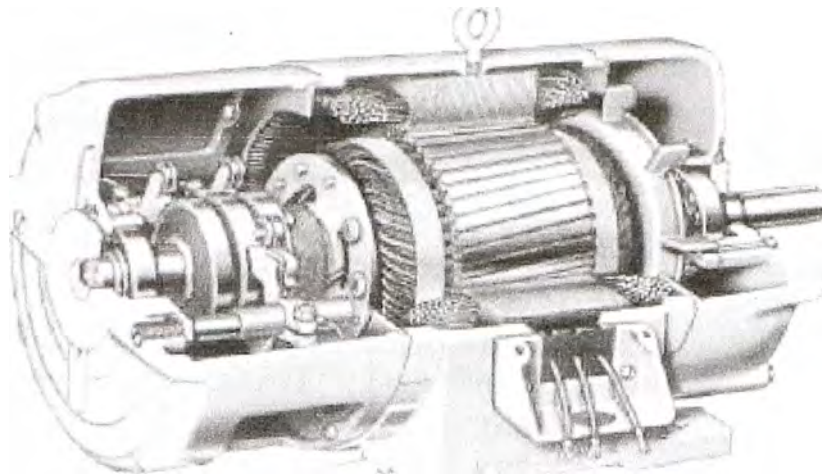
Máquina de inducción de rotor bobinado con anillos deslizantes [9]
